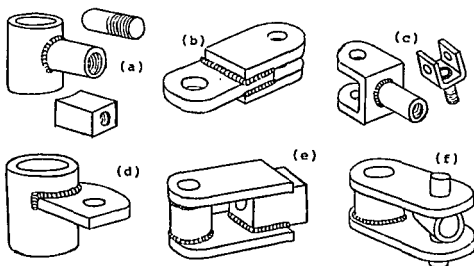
Miembros de unión y orquillas soldadas.
